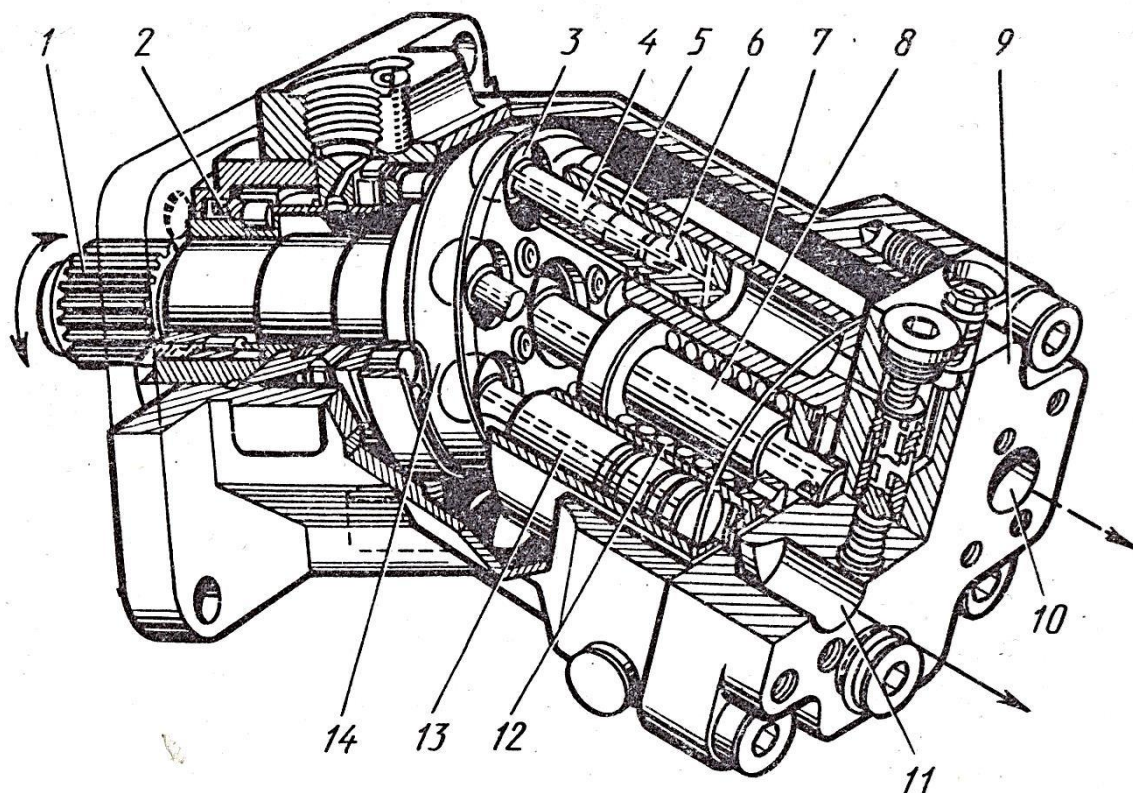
Аксиально-поршневой нерегулируемый насос-гидромотор с реверсивным потоком и наклонным блоком:
